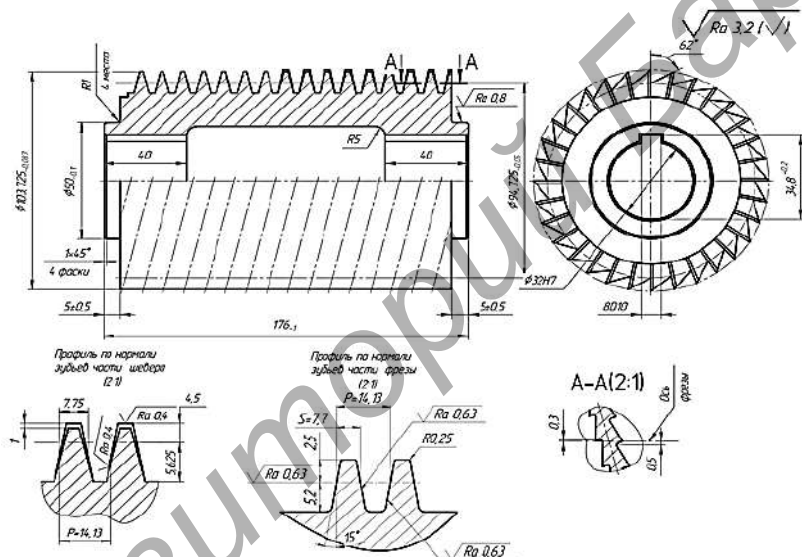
Чертеж комбинированного инструмента — червячная фреза-шевер
